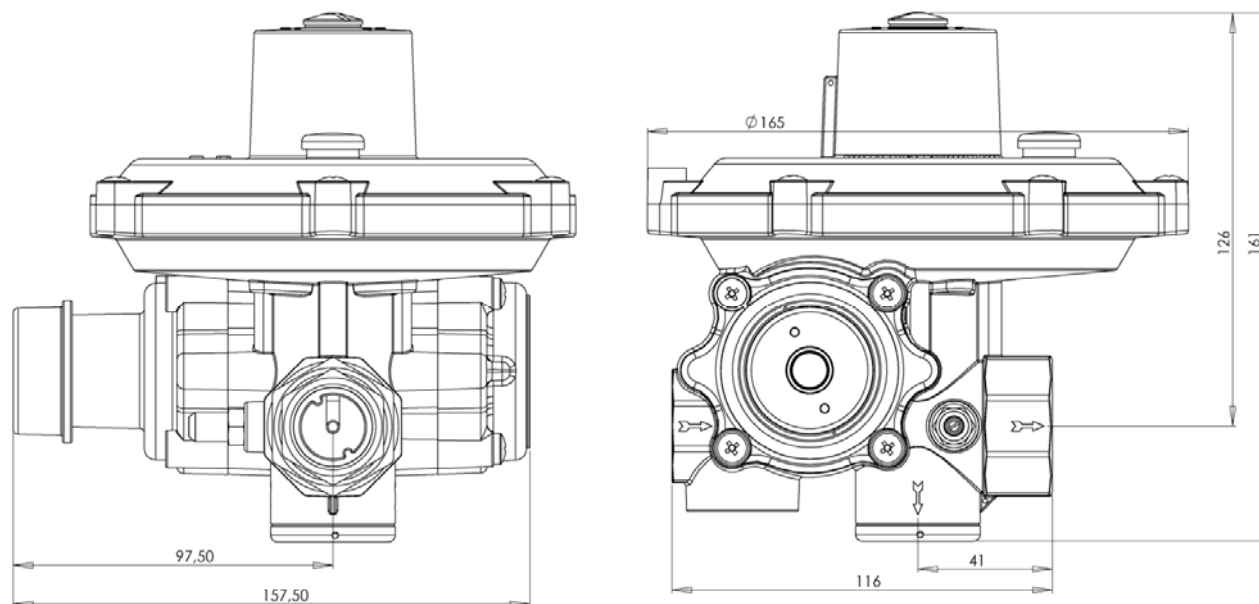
Dimensiuni constructive ale RTG 25 C cu supapă de blocare
